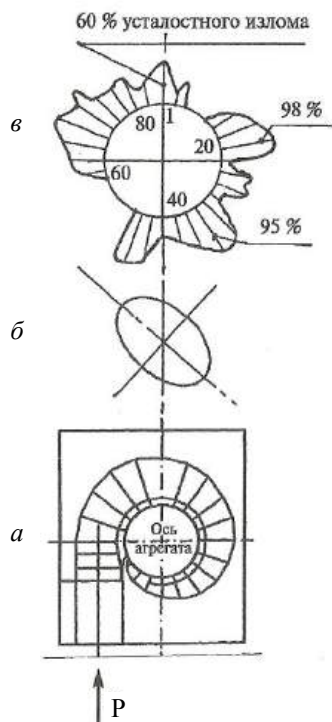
Механизм возникновения срезающих напряжений в шпильках крепления крышки рабочего колеса:
